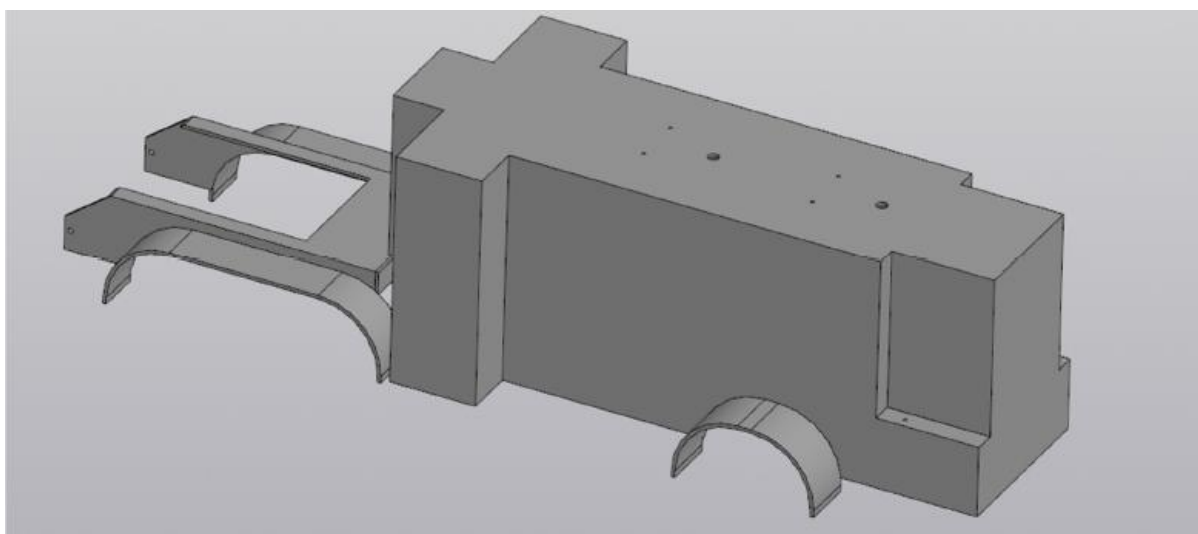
3D-модель части корпуса, накрывающей тягач
